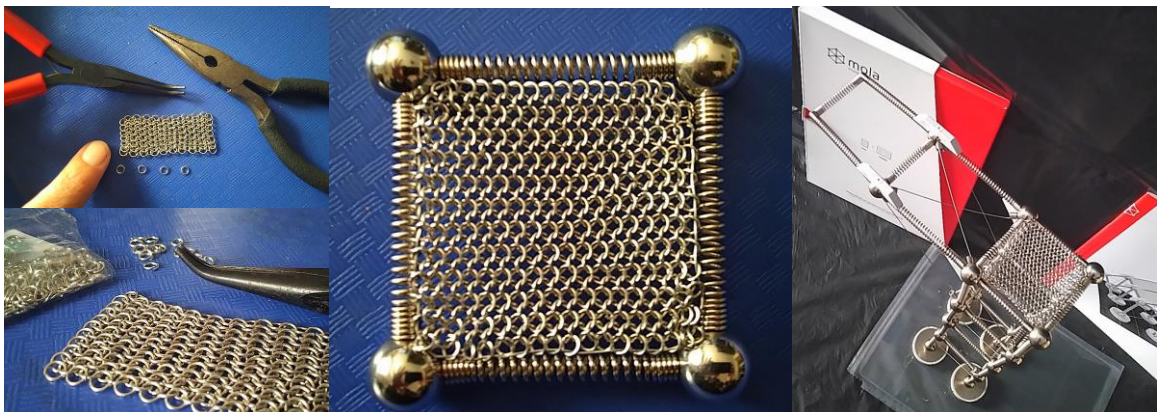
Construcción de la cota de malla, emplazamiento y puesta en maqueta.
